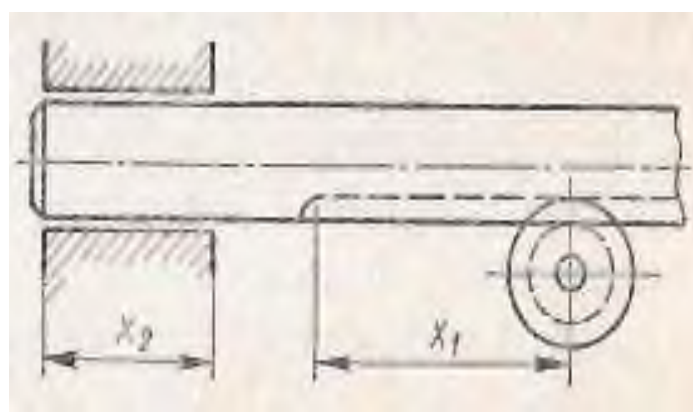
Ошибки конструкции: длина зубчатой рейки недостаточна, так как перемещение рейки x_1 больше длины опоры x_2 [5]
